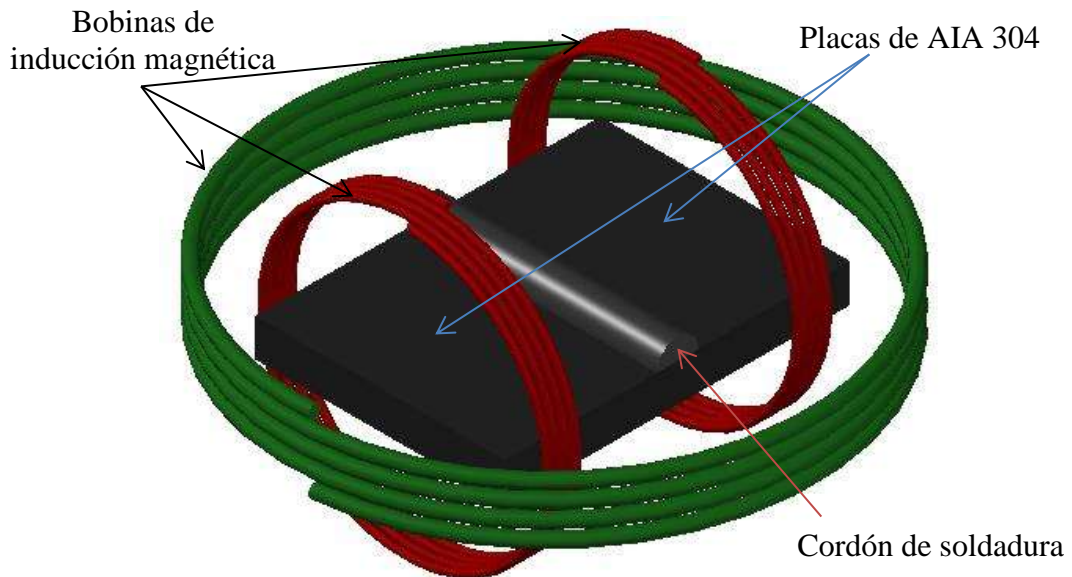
Esquema representativo de la configuración combinando los campos magnéticos perpendicular y axial a la dirección de aplicación del cordón de soldadura.
